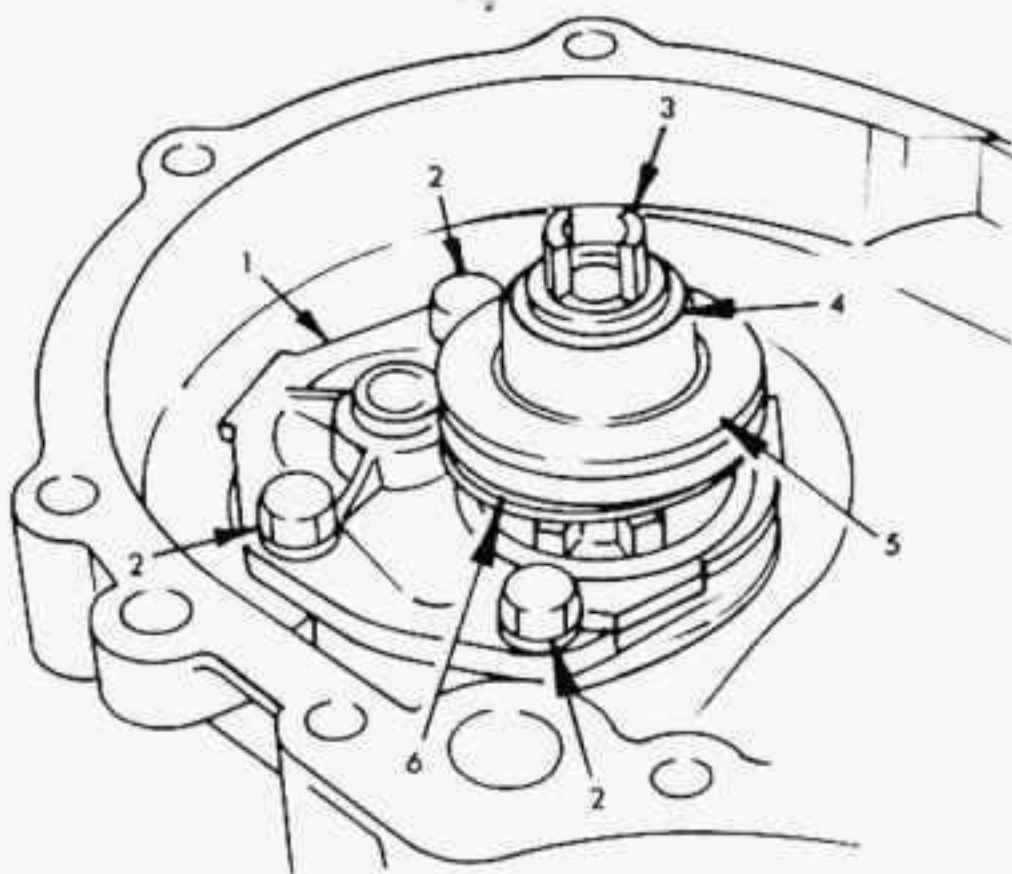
Steuerungsdeckel mit Ölpumpe und Überdruckventil
